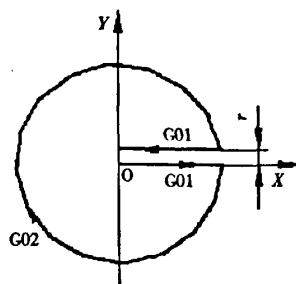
用 G42 加工内孔后接 G01 时的刀心轨迹
